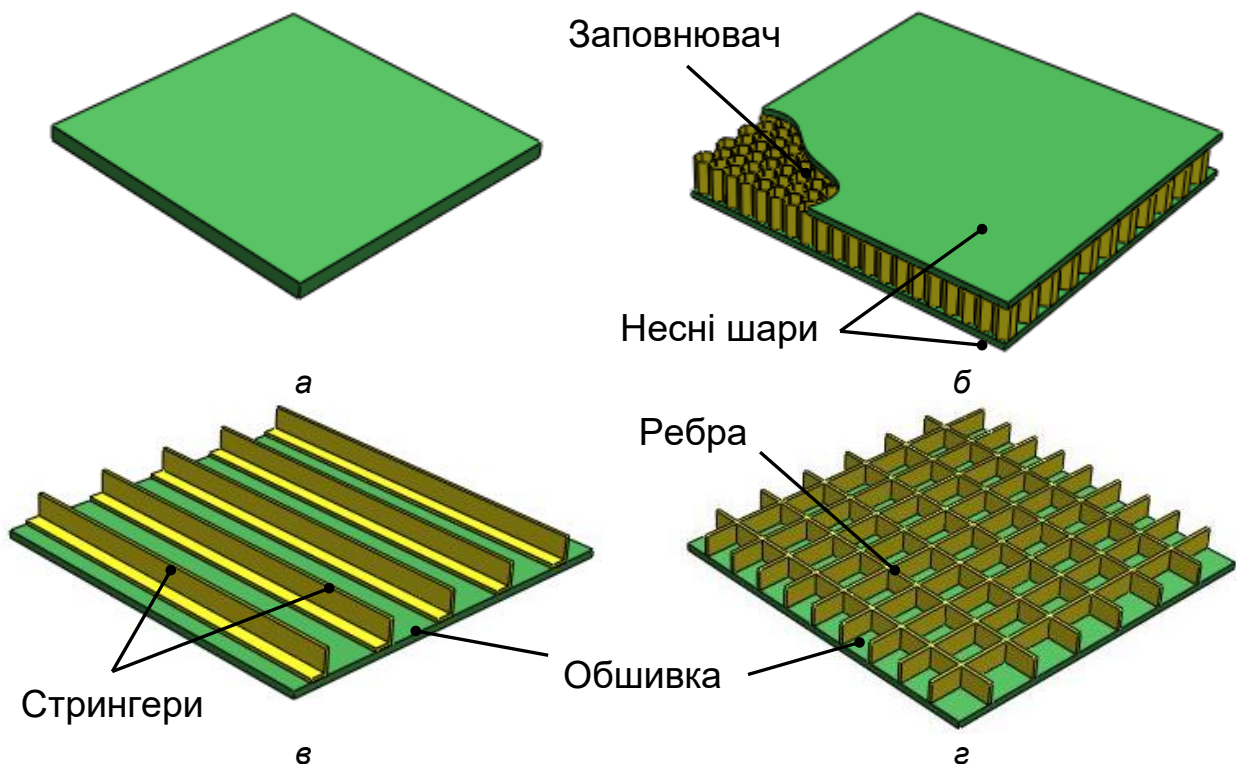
Типи панелей: а – гладка шарувата; б – панель із заповнювачем; в – підкріплена (стрингерна); г – вафельна
